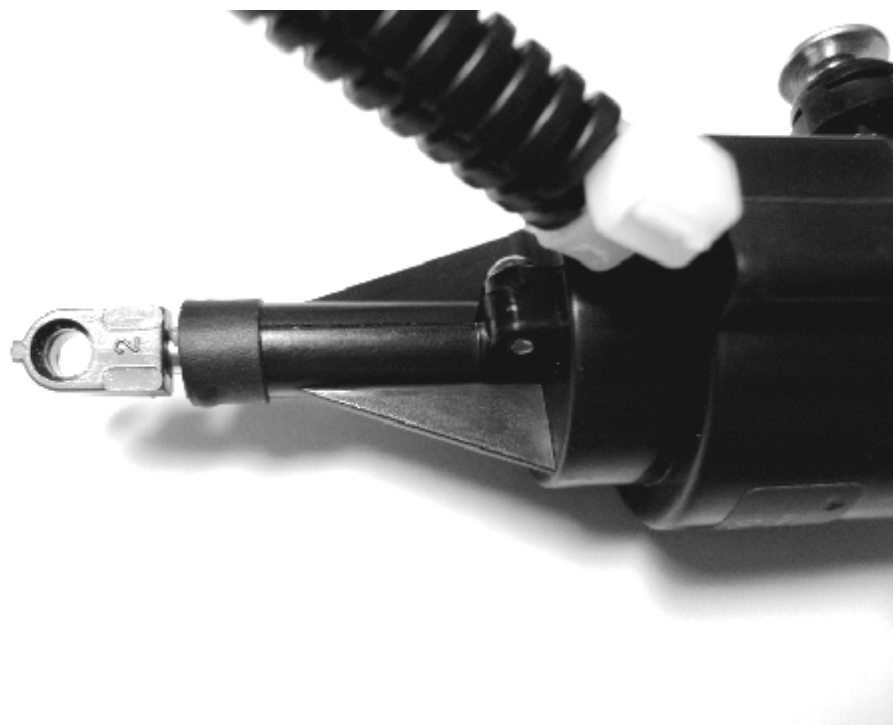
Отверстие крепления штока моторедуктора.
